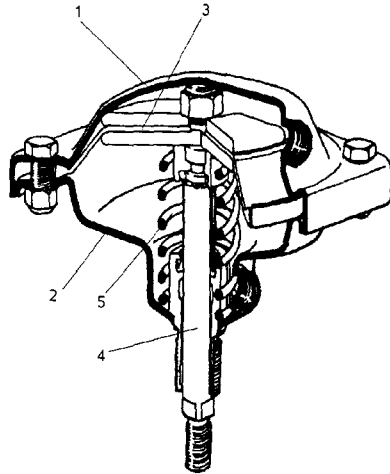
Niektoré možné vyhotovenia jednočinných pneumatických motorov
